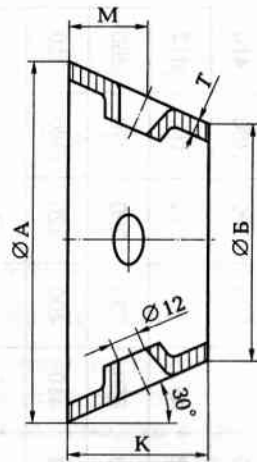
Эскиз детали из листового алюминиевого сплава
